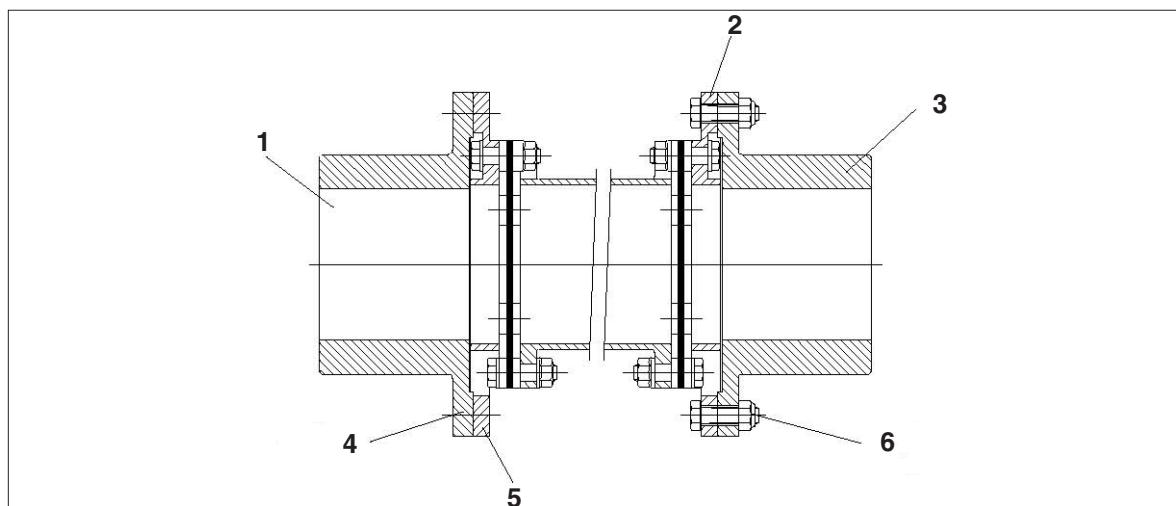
Резьбовое соединение фланцев "С" и "F"
